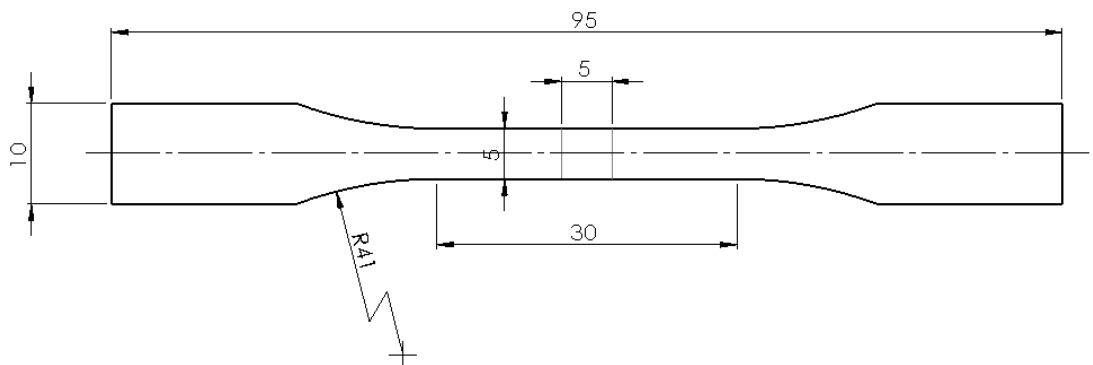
Desenho técnico dos provetes para ensaio de tração uniaxial.
